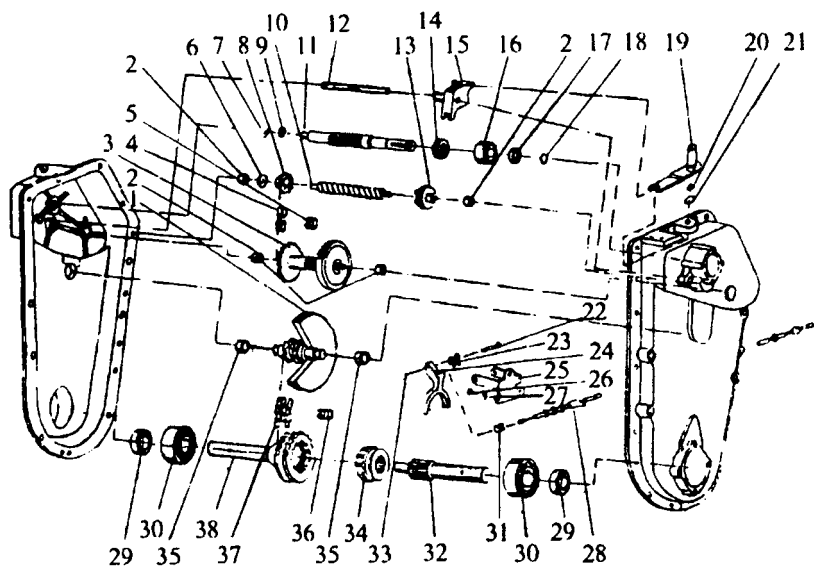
Редуктор МБ-2, внутреннее устройство:
